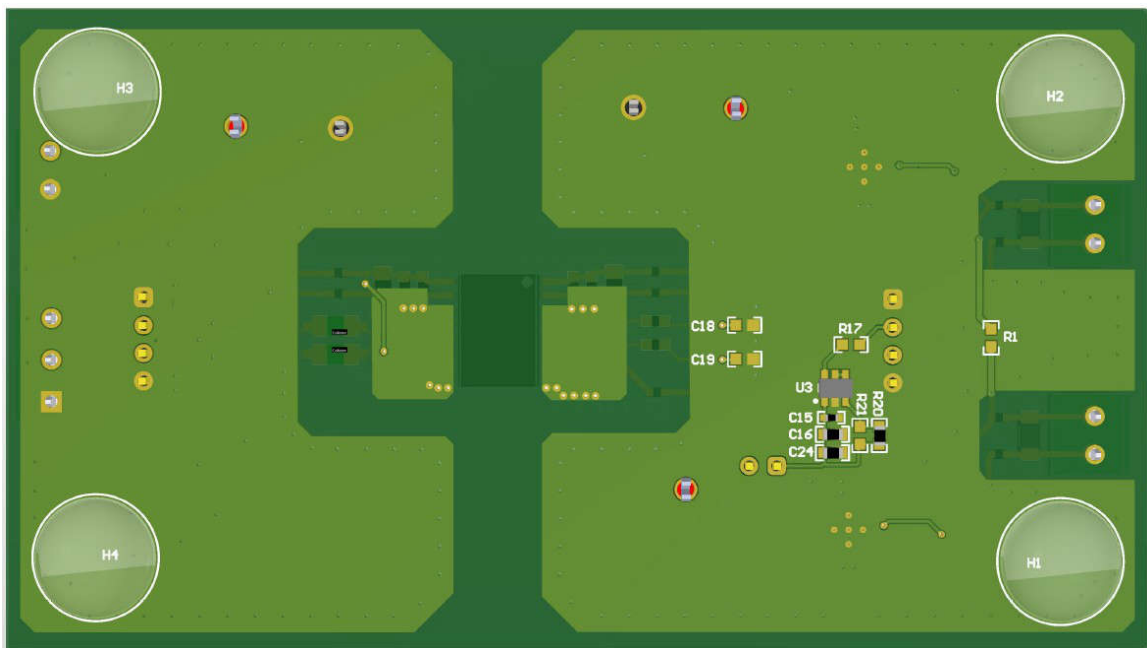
ISOW1050DWEEVM PCB 3D 视图 - 底层
